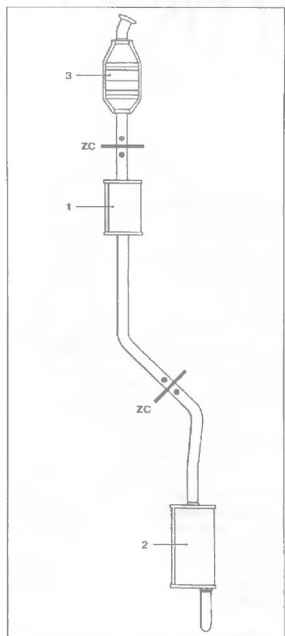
Трубопроводы системы выпуска отработавших газов и расположение зон резы: 1 – Передний глушитель; 2 – Основной глушитель; 3 – Каталитический нейтрализатор; ZC – Зона резы трубы.
